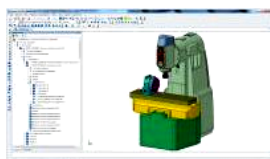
3D-модель багатоопераційного верстата СВМ1Ф4
